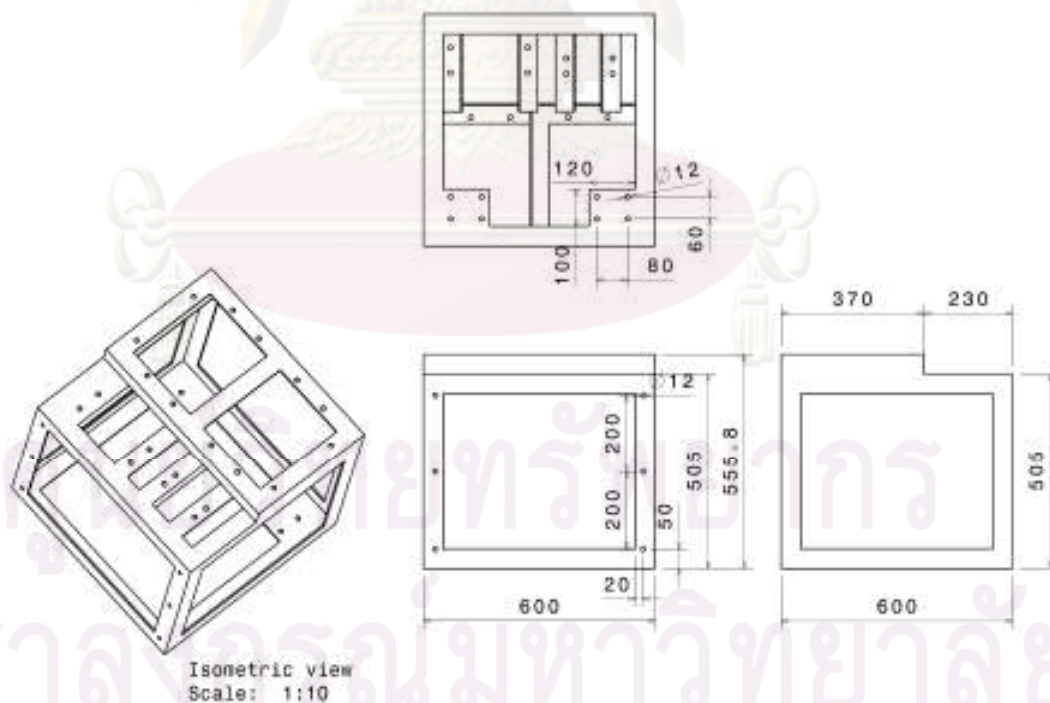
แบบ Drawing ของ Port valve 2
